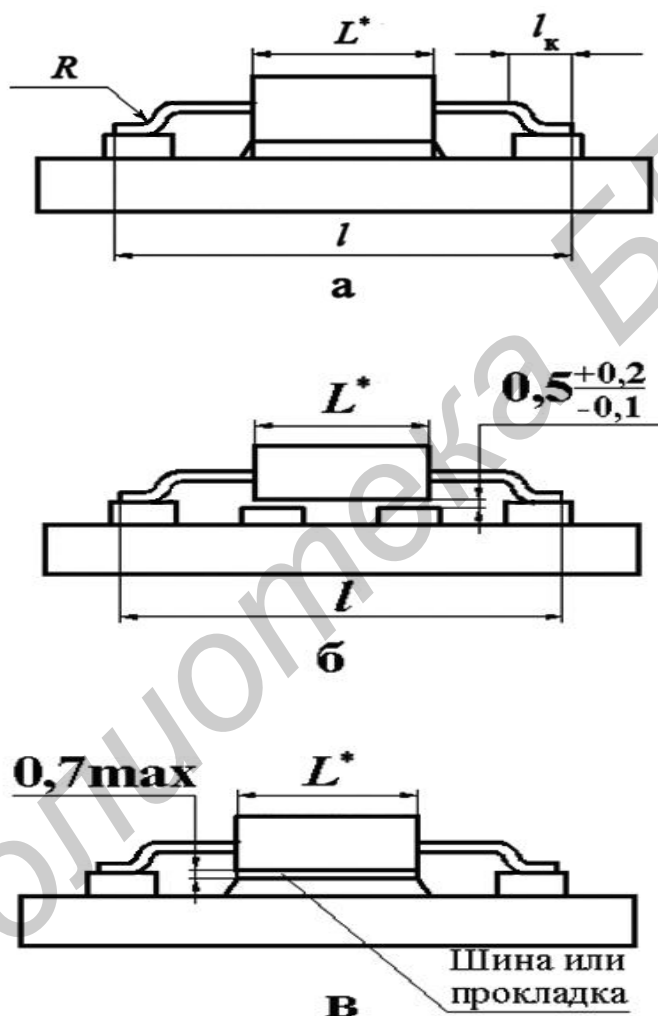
Формовка выводов и установка ИЭТ с планарными выводами типовых конструктивных исполнений 36–38 (\* размер для справок):
